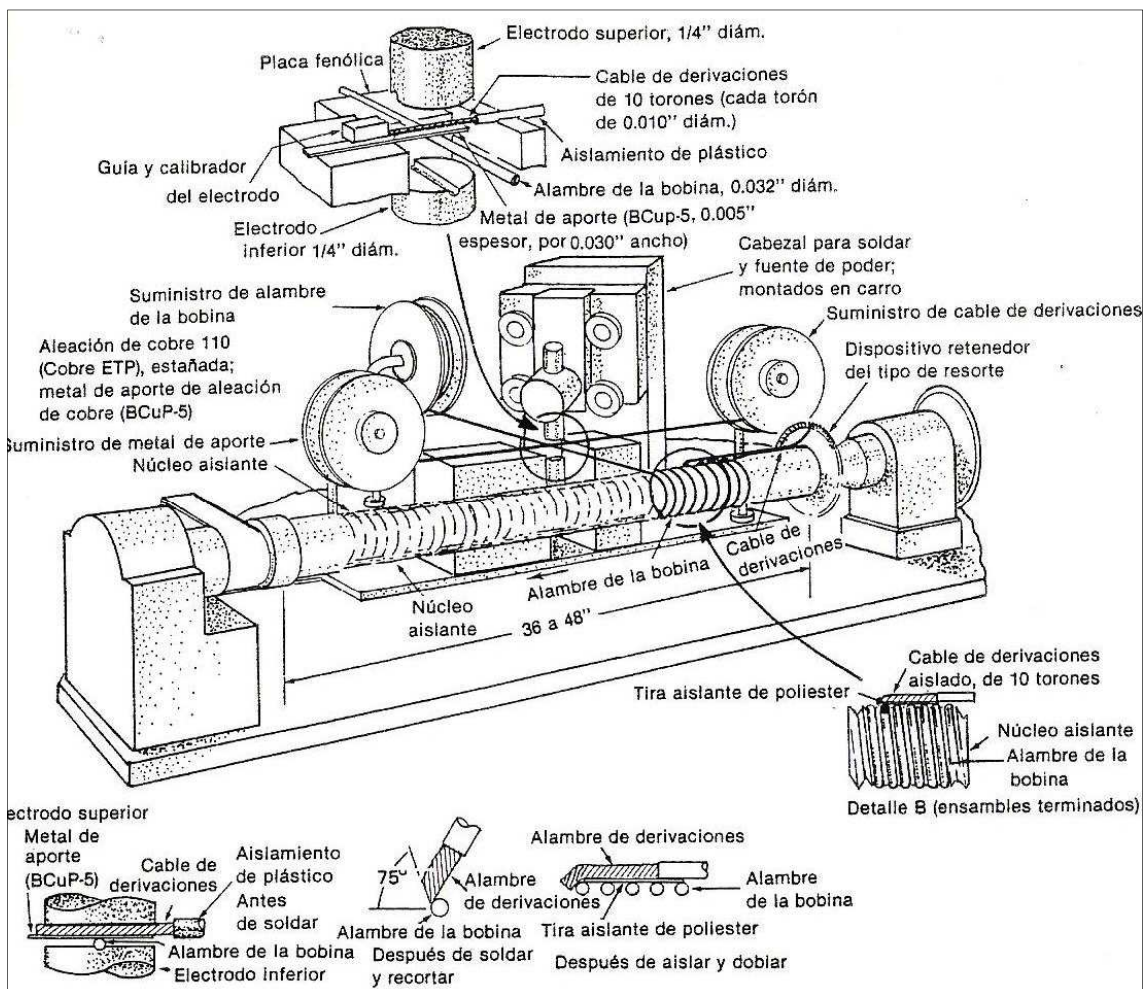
Fuente <http://soldadurafuerte.blogspot.com/>
